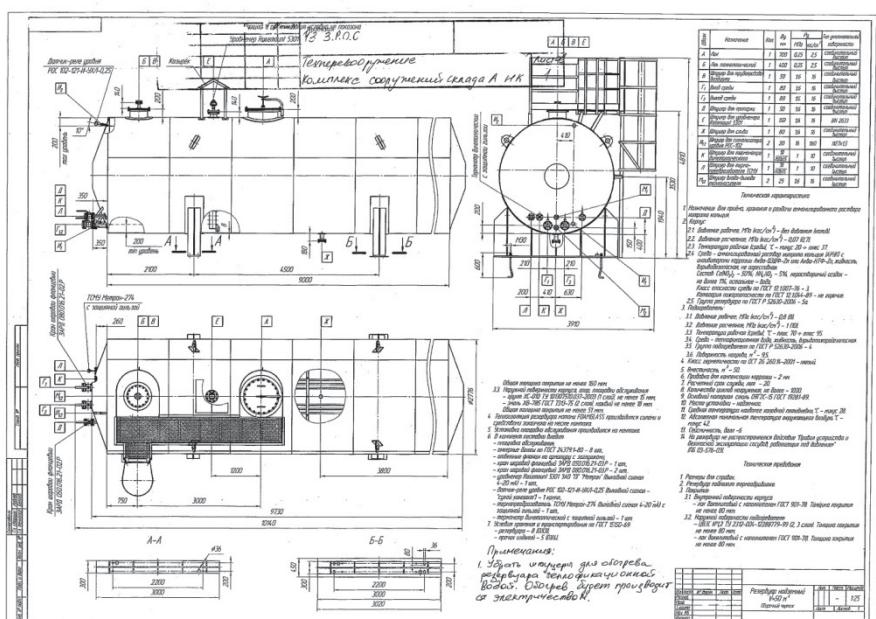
Чертеж резервуара, подлежащего обогреву.
